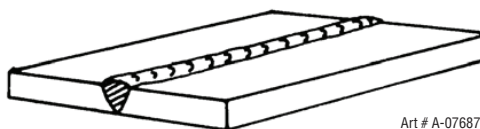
Position à plat, soudure par aboutement à l'horizontale
